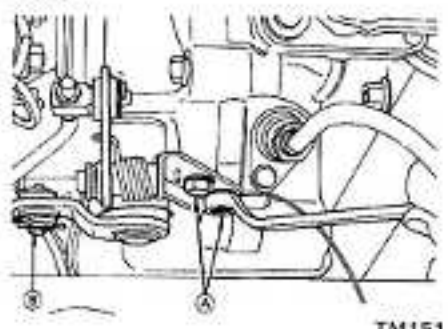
Dépose de la manivelle de sélection et de la tige de déplacement
